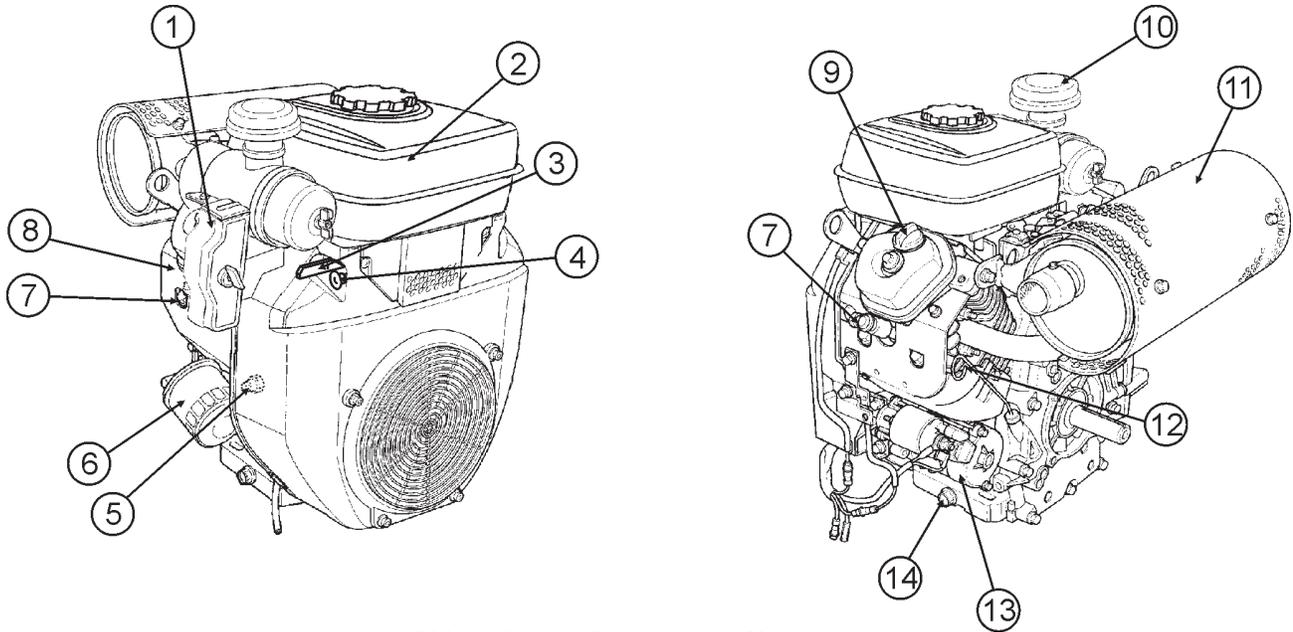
Steuerelemente und Komponenten des Motors (Honda GX620TXF2)
